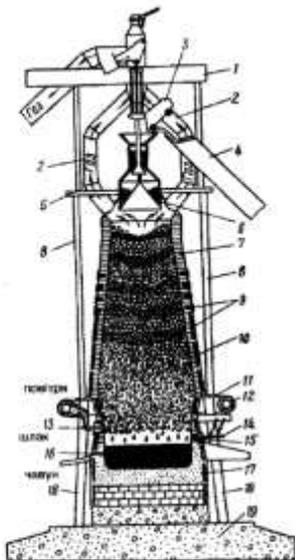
Розріз доменної печі: 1 - копер; 2 - газозвідді; 3 - скіп; 4 - похилний міст; 5 - колошниковий майданчик; 6 - засильний апарат; 7 - шамотна футеровка; 8 - колона; 9 - холодильники; 10 - броня; 11 - маратор; 12 - кільцевий повітропровід; 13 - фурма; 14 - шлаковий стопор; 15 - шлакова летка; 16 - чавунна летка; 17 - кладка вуглецева; 18 - основна колона; 19 - фундамент
